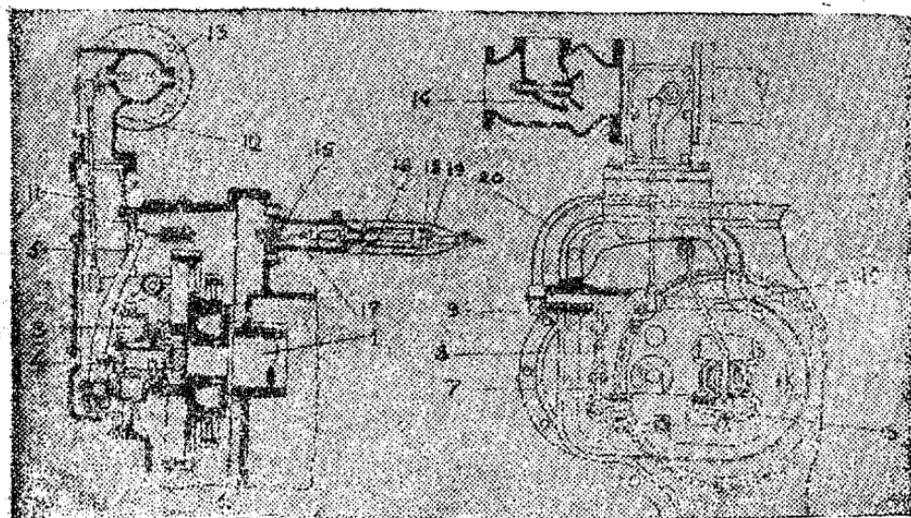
Регулятор (продольный разрез и вид спереди): 1—распределительный вал; 2—шестерня распределительного вала; 3—грузик регулятора; 4—муфта регулятора; 5—рычаг регулятора длинный; 6—валик рычагов; 7—рычаг регулятора короткий; 8—тяга вилчатая; 9—рычаг двулучи; 10—валик ограничителя; 11—тяга к дроссельной заслонке; 12—корпус дроссельной заслонки; 13—дроссельная заслонка; 14—смеситель; 15—пружина регулятора; 16—тяга пружины; 17—кронштейн-кожух; 18—регулировочная гайка; 19—контргайка; 20—наружный рычаг ограничителя.
